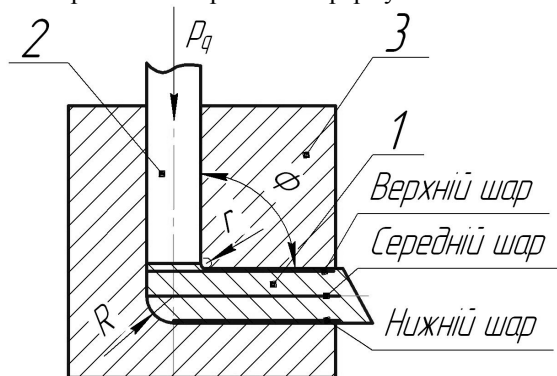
Схема РККП (1 – заготовка, 2 – пуансон, 3 – матриця)
